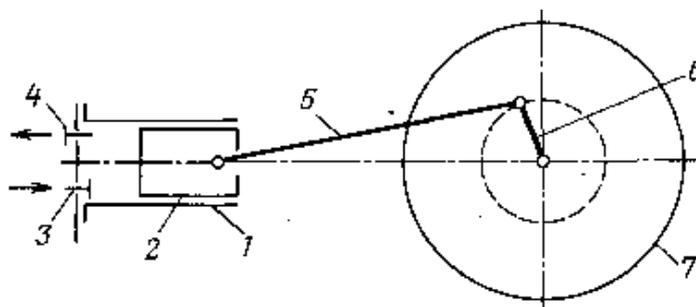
Одноцилиндровый компрессор простого действия: 1 – цилиндр, 2 – поршень, 3 – всасывающий клапан, 4 – нагнетательный клапан, 5 – шатун, 6 – кривошип, 7 – маховик
